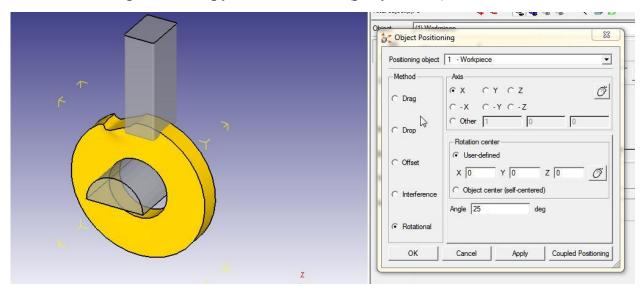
Установки для поворота заготовки вокруг оси Х.
